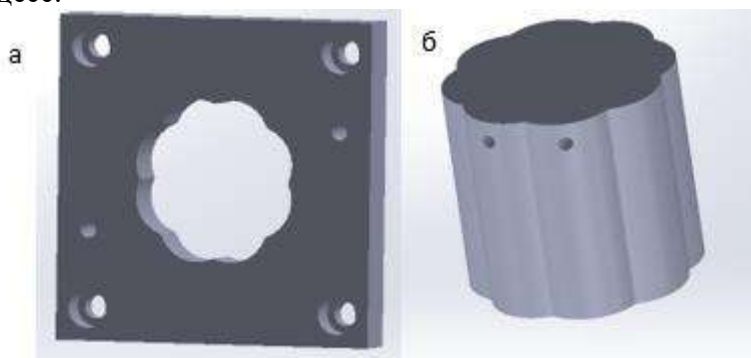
Формообразующие детали: а – матрица; б - пуансон для вырубки.
